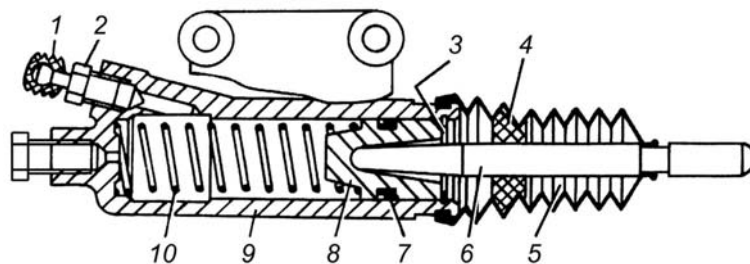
Рабочий цилиндр привода выключения сцепления: 1 - колпачок защитный; 2 - клапан перепускной; 3 - кольцо стопорное; 4 - кольцо защитное; 5 - чехол; 6 - толкатель; 7 - манжета; 8 - поршень; 9 - корпус цилиндра; 10 - пружина;
